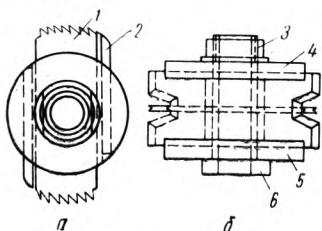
Комбинированная фрезерная головка (а — вид сверху; б — вид сбоку):
